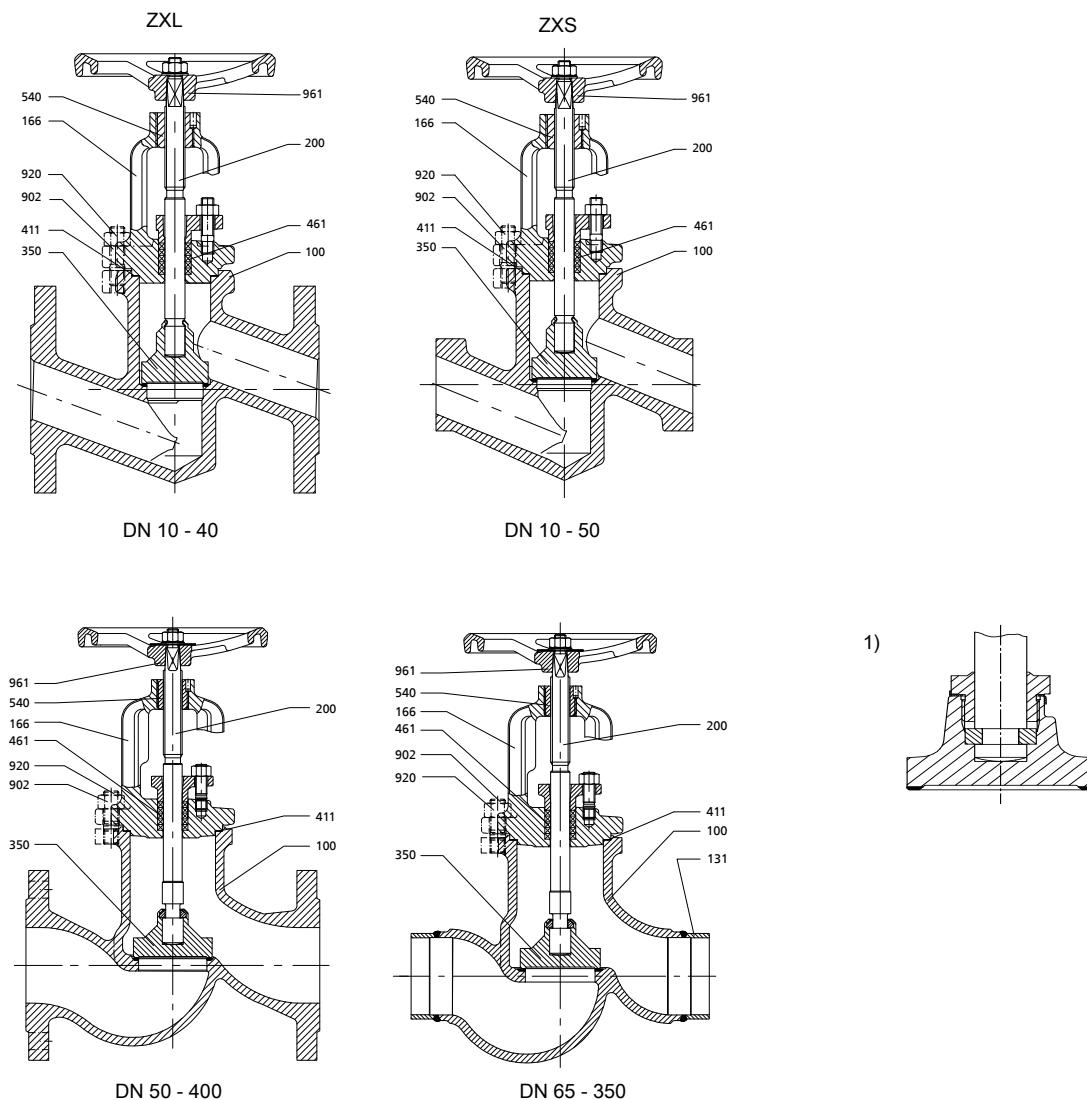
Разрез; 1) Начиная с DN 125, резьбовое крепление конусного золотника
